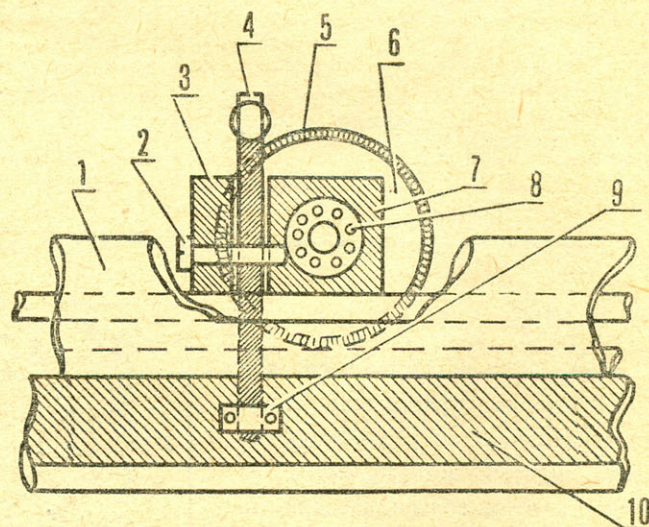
КРЕПЛЕНИЕ ТОКОСЪЕМНИКА (вид сбоку):
